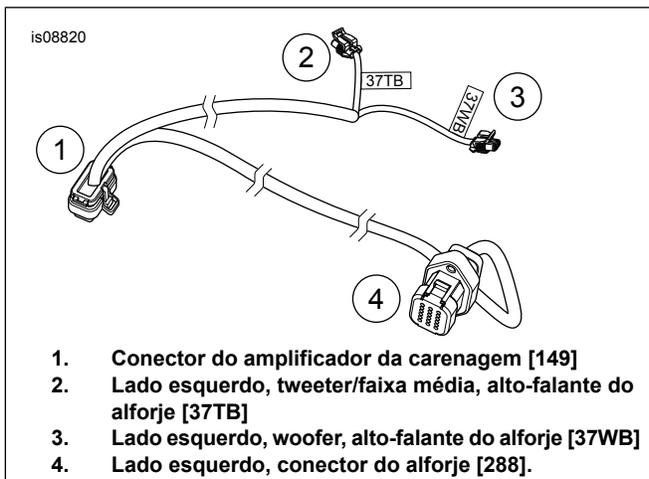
Chicote de fios, alto-falante do alforje do lado esquerdo
